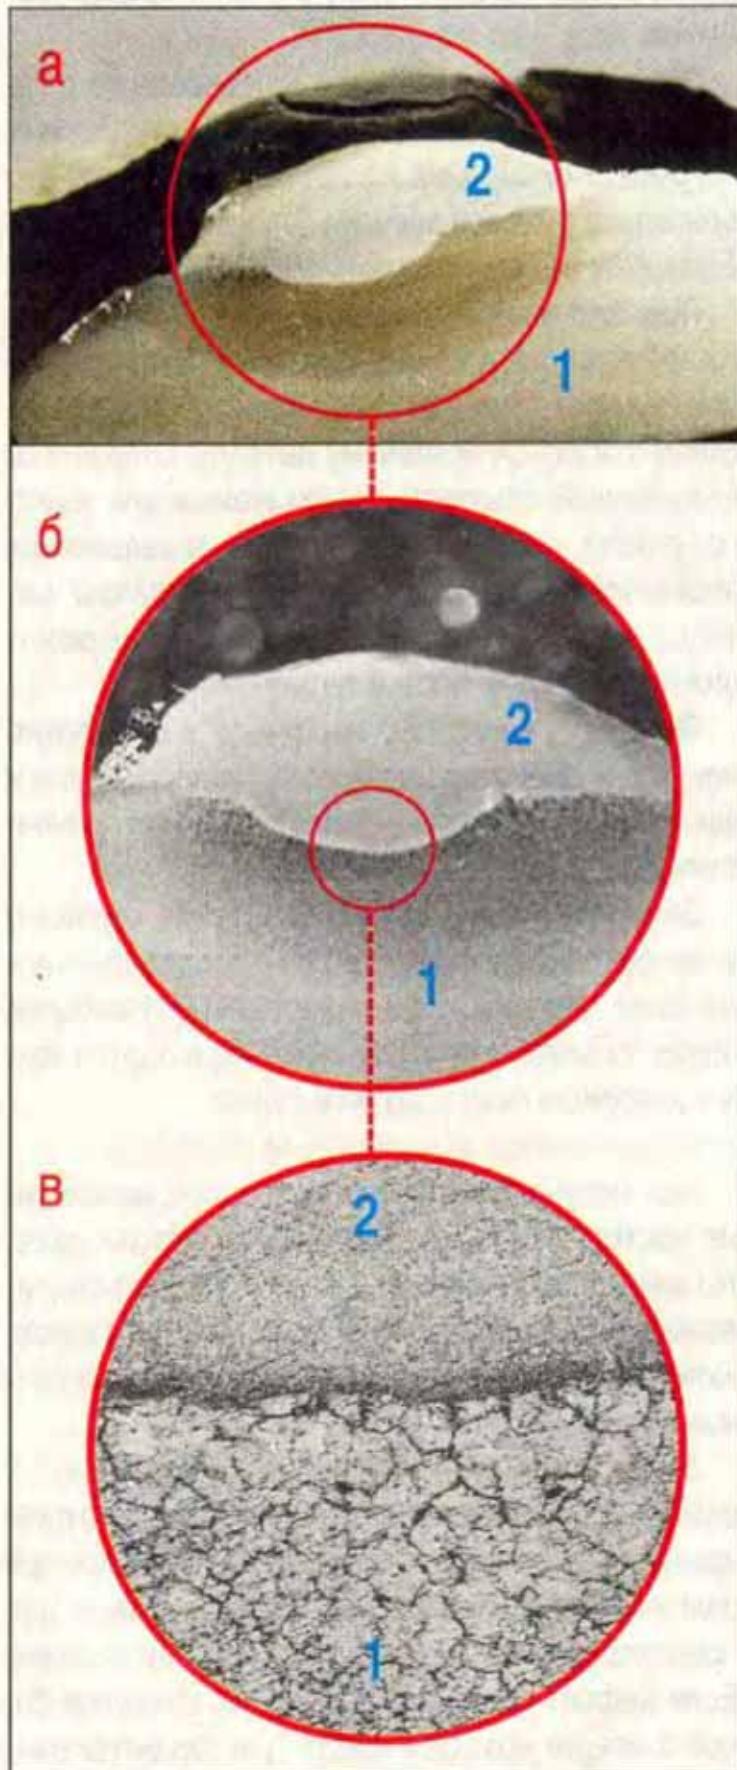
Разрез сварного шва: а – отшлифованный образец, вырезанный из сварного шва (микрошлиф); б – граница между металлом литьей детали и металлом шва; в – зона структурных изменений, прилегающая к сварному шву; 1 – деталь; 2 – сварной шов.
